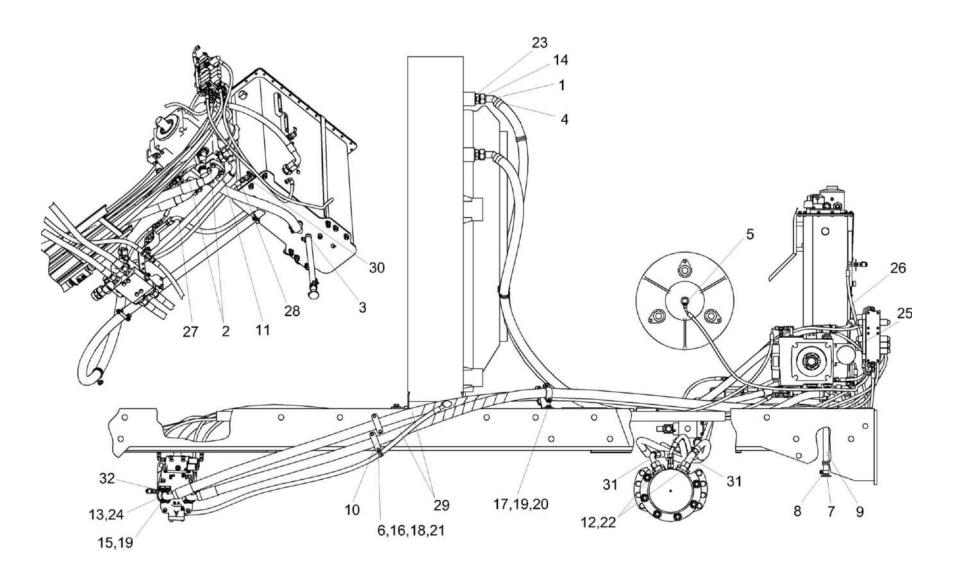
Гидросистема привода ходовой части КВК-2-0601000 (вид сбоку)
